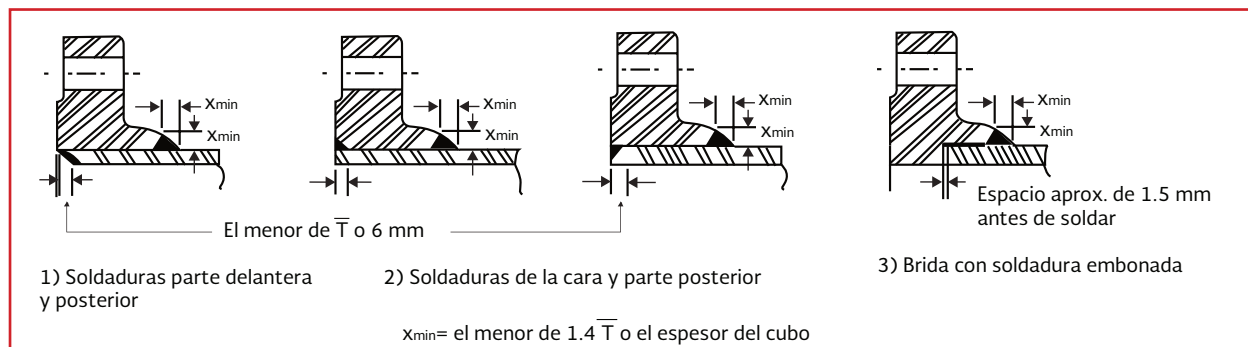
Detalles típicos para bridas con accesorios soldados con soldadura tipo deslizante doble y embonada.
